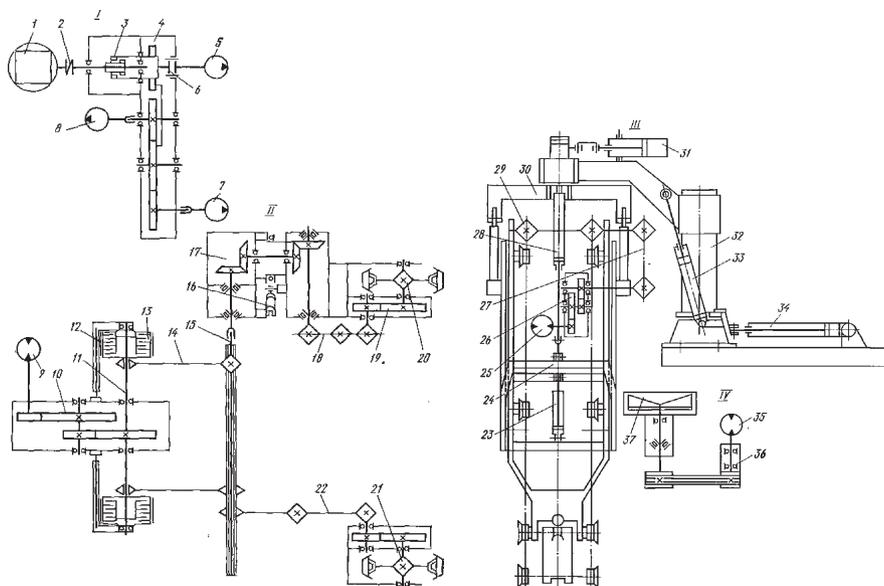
Кинематическая схема каналоочистителя МР-15: I-IV — приводы насосов, передвижения, рабочего оборудования, метателя; 1 — дизель; 2 — муфта сцепления; 3, 6 — зубчатые муфты; редукторы: 4 — привода насосов, 10 — хода, 17 — вспомогательной гусеницы, 19 — бортовой, 26 — рабочего органа; насосы: 5 — хода, 7 — рабочего органа, 8 — управления; гидромоторы: 9 — хода, 25 — ковшовой цепи, 35 — метателя; валы: 11 — хода, 15 — телескопический, 29 — Приводной; 12 — тормоз; 13 — фрикцион; 14, 18, 22, 27 — целные передачи; гидроцилиндры: 16 — поворота вспомогательной гусеницы, 23, 38 — выдвигения и наклона рабочего органа, 31, 34 — поворота подвески и колонны, 33 — подъема рабочего органа; 20, 21 — ведущие звездочки вспомогательной и основной гусеницы; 24 — рабочий орган; 30 — портал; 32 — пилон; 36 — ременная передача; 37 — метатель
